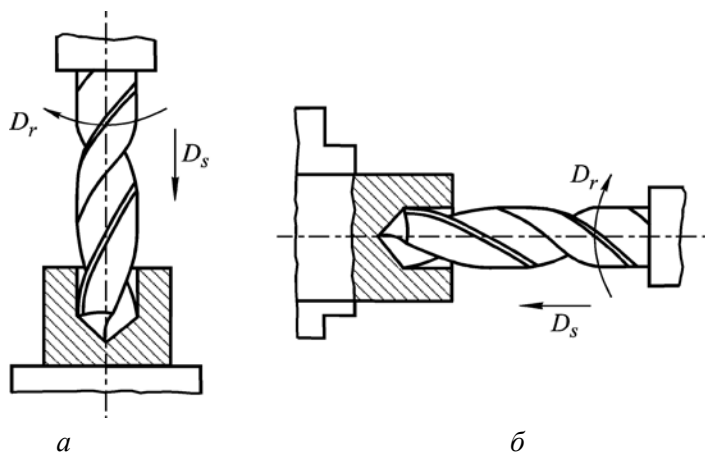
Схемы обработки отверстий на сверлильных (а) и токарных (б) станках
